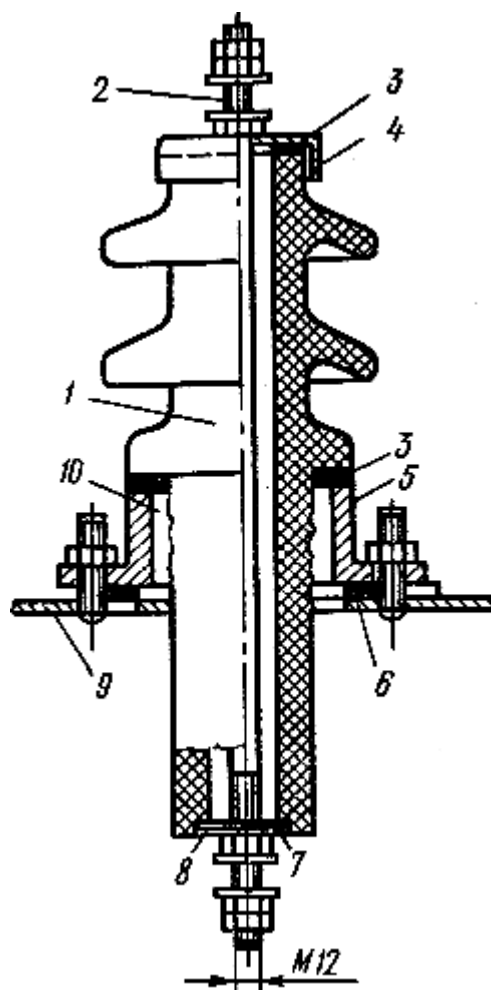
Армированный ввод 6-10 кВ наружной установки:
